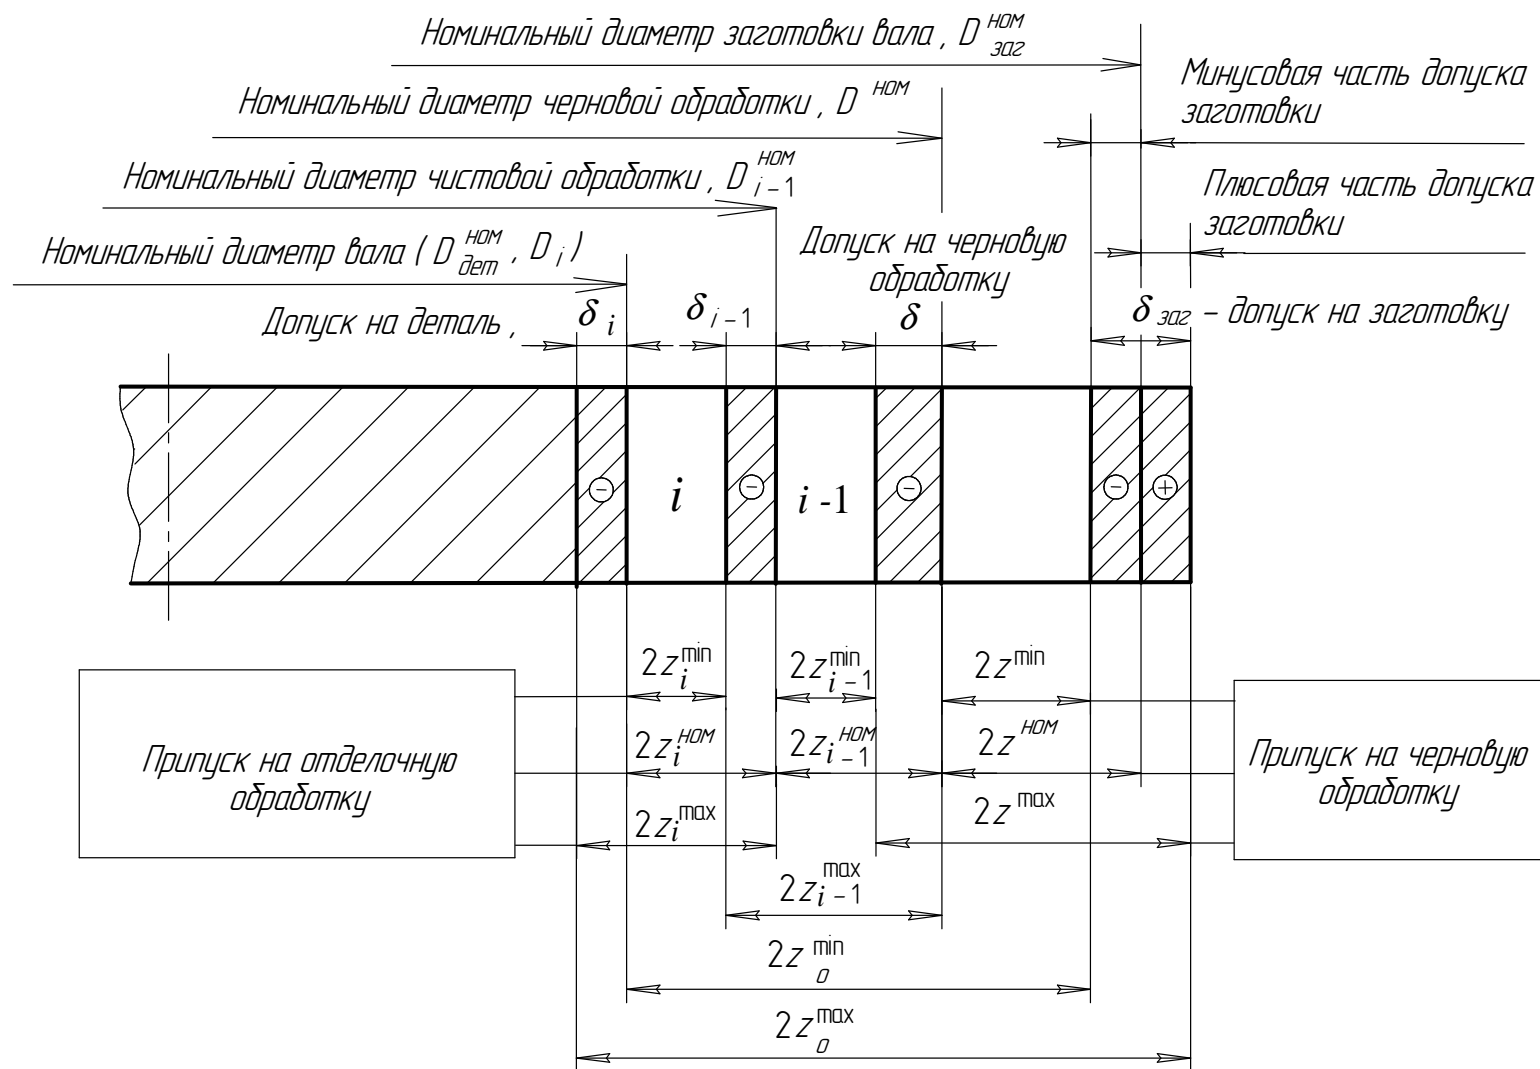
Схема расположения припусков и допусков при обработке наружной цилиндрической поверхности вала
